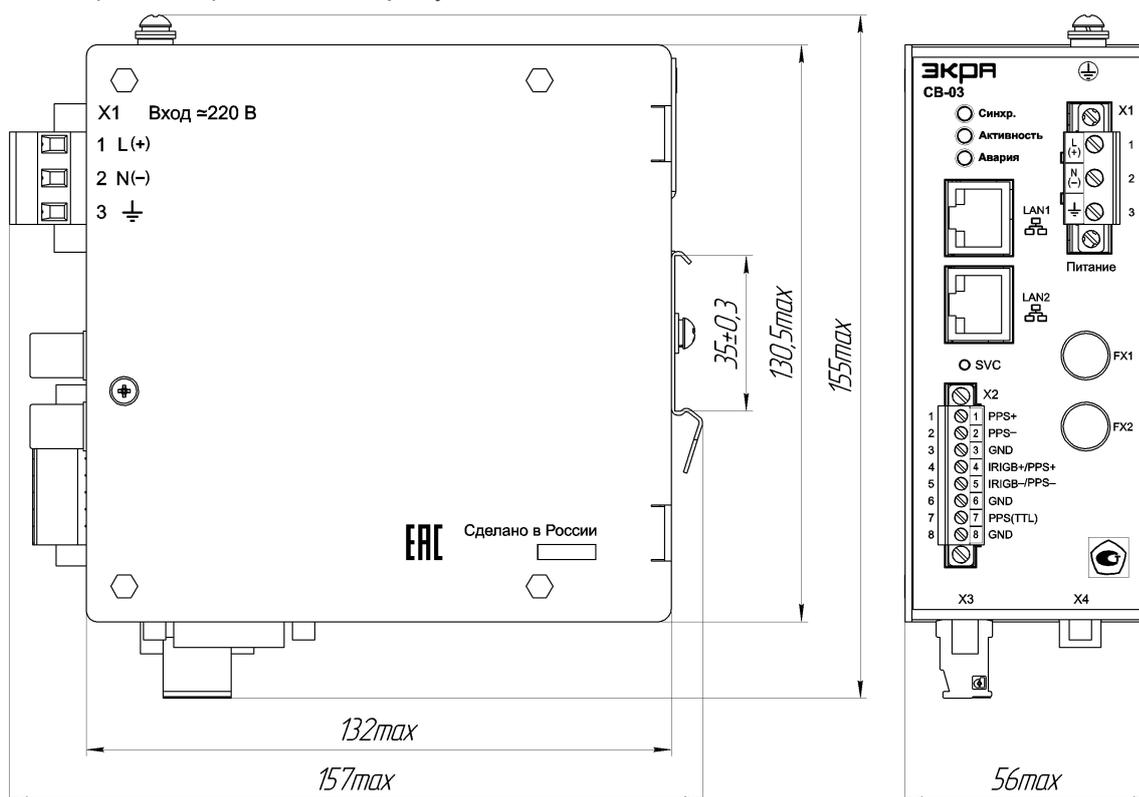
Общий вид устройства СВ-03 (без исп.)
